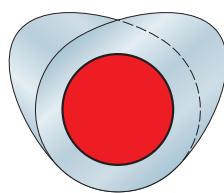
Положение кулачков первого цилиндра при укладке распределительного вала в опоры головки блока цилиндров
